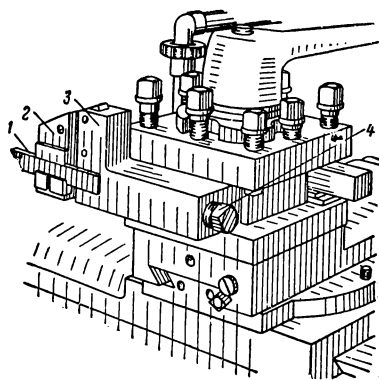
Специальная державка для крепления пластинчатых отрезных резцов.
